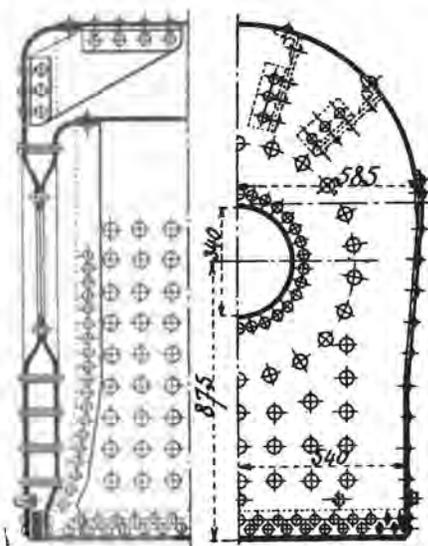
Face arrière de la boîte à feu des locomotives du type 7 du Nord-Empeur-Ferdinand; le cadre de la porte du foyer est remplacé par l'assemblage de pincettes relevées dans les deux plaques.
